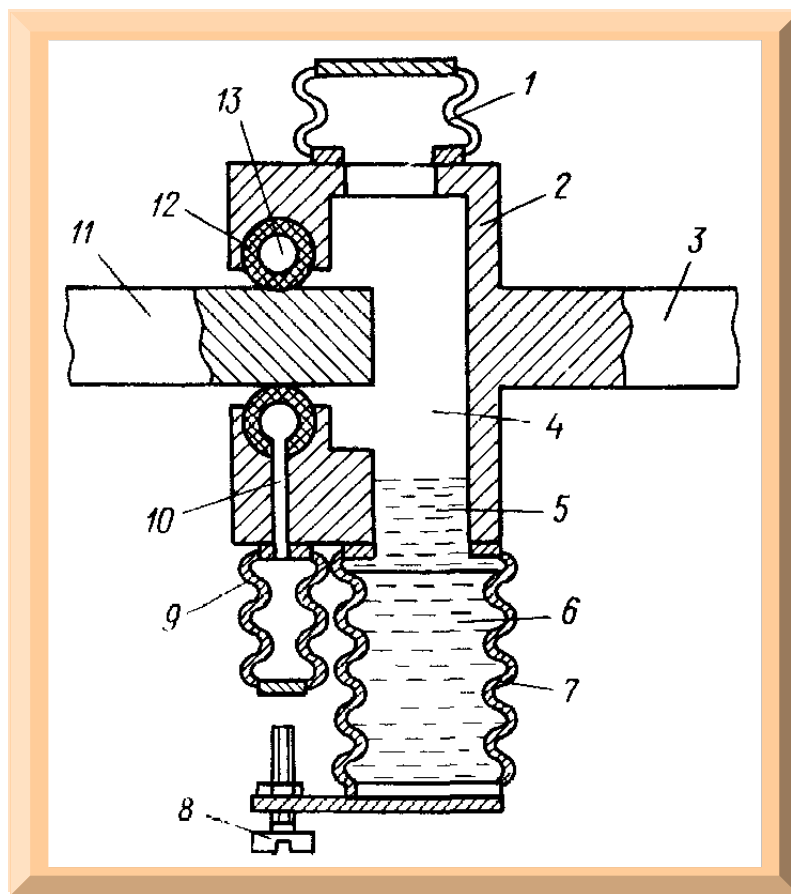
Разъединитель для подвода тока к деталям, не допускающим какого бы то ни было механического воздействия
